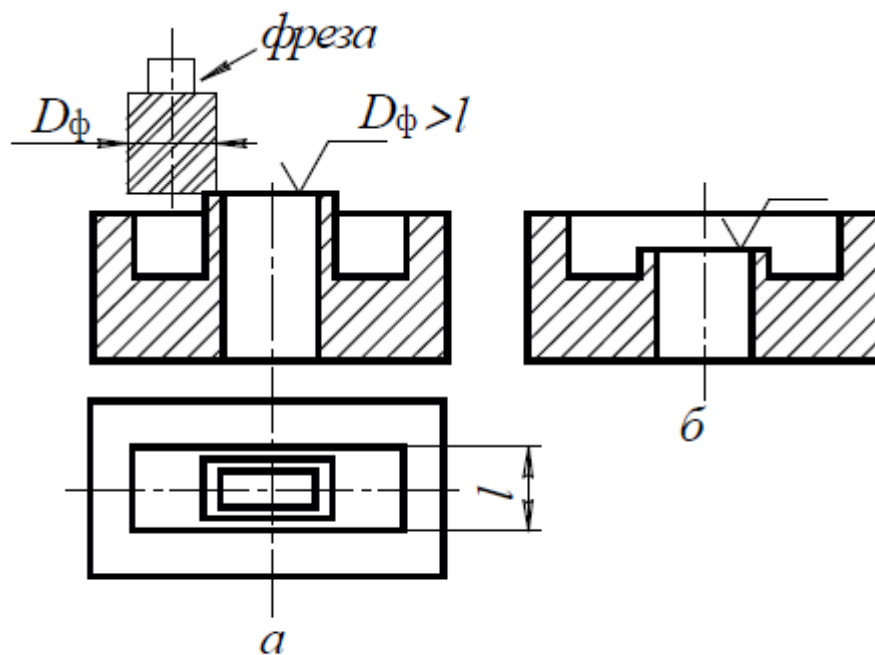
Конструкция корпусных деталей с пазом и бобышкой:
